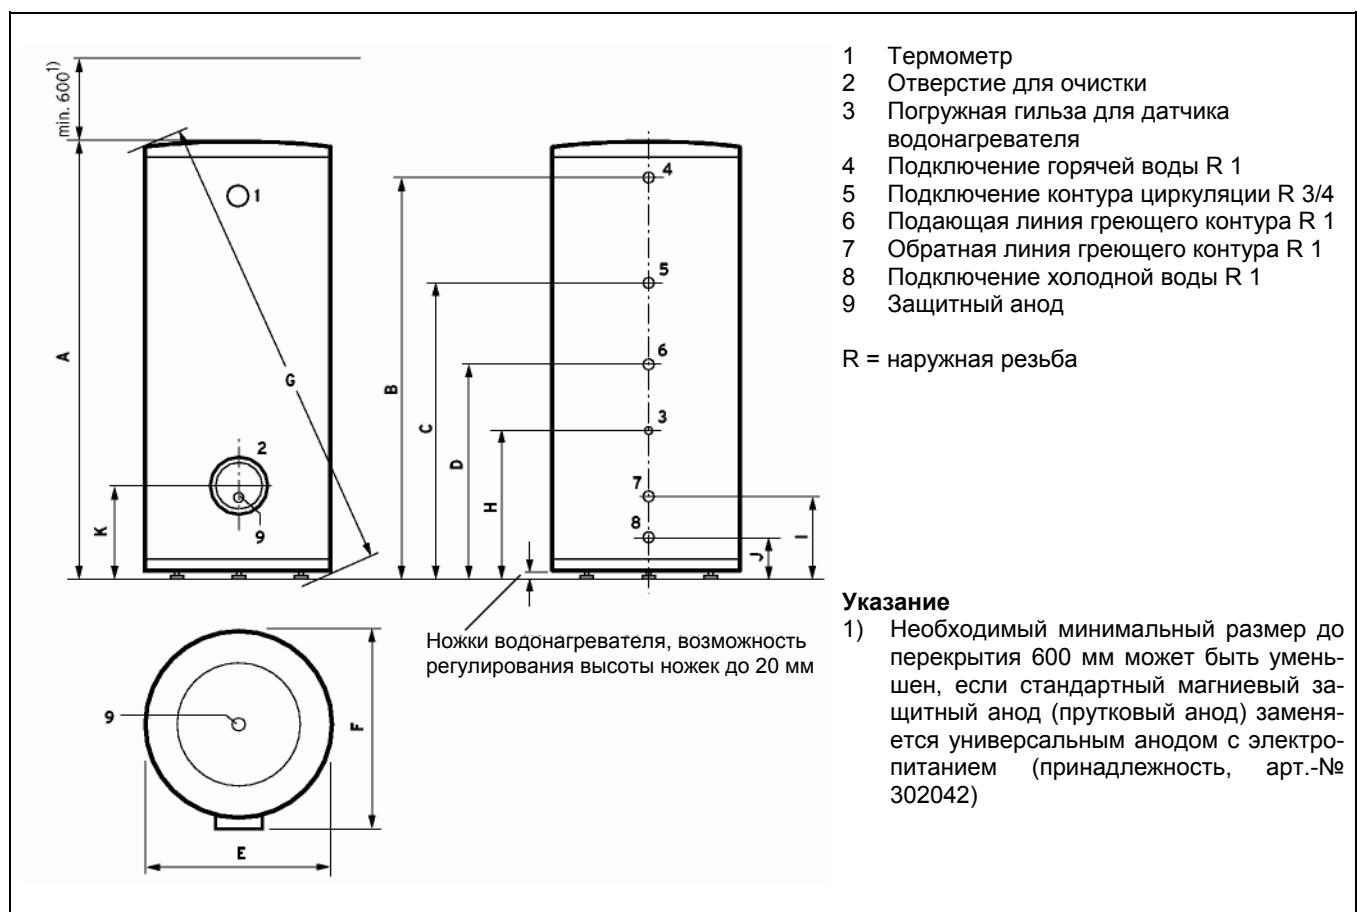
Размеры водонагревателей VIH .../7 и присоединительных патрубков
